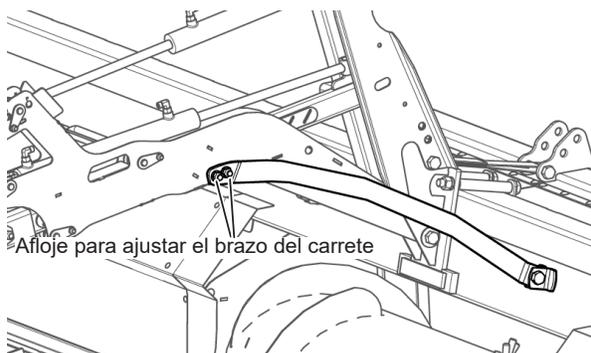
Centrado del carrete - soporte del brazo del carrete central
